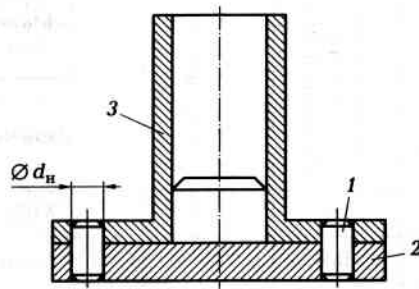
Сборочный чертеж соединения деталей 2 и 3 с помощью двух запрессованных штифтов
